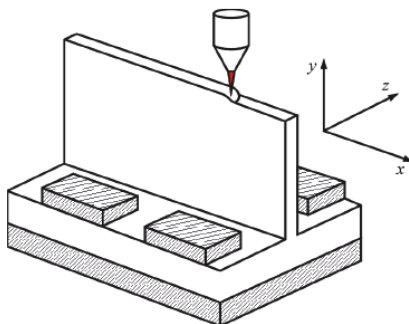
Схема пошарового формування балкової конструкції таврового профілю за технологією xBeam 3D Metal Printer
